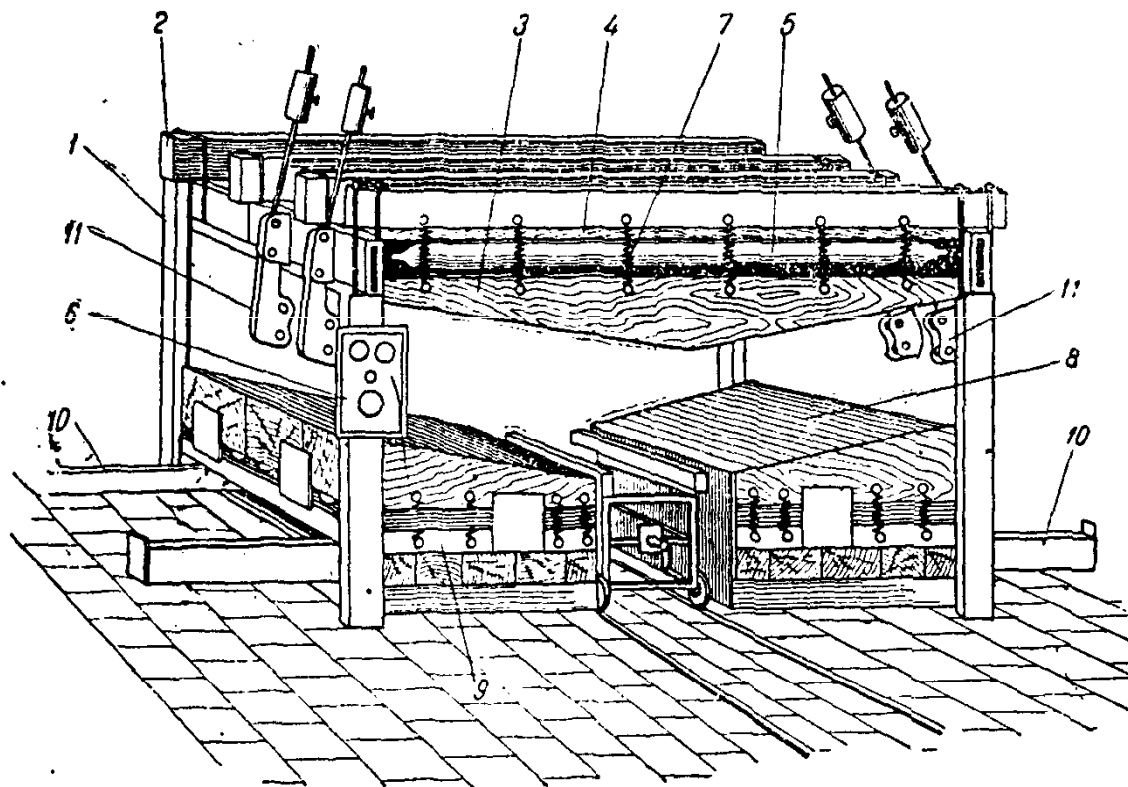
Установка лобовой обшивки на каркас центроплана винтовой запрессовкой.
